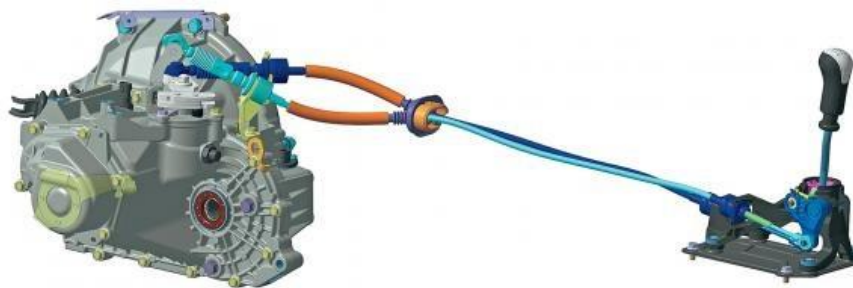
Тросовый привод коробки передач ВАЗ-21807
